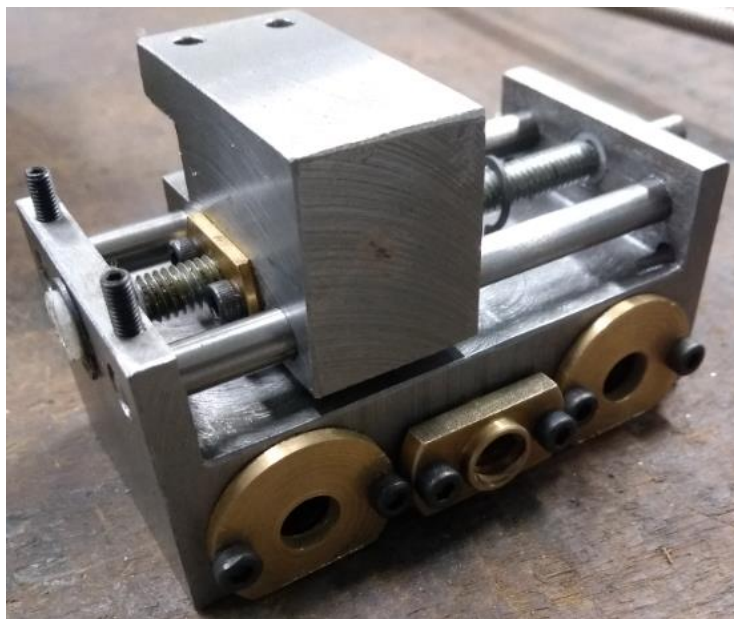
montagem dos carros transversal e longitudinal (Fonte: acervo próprio).
